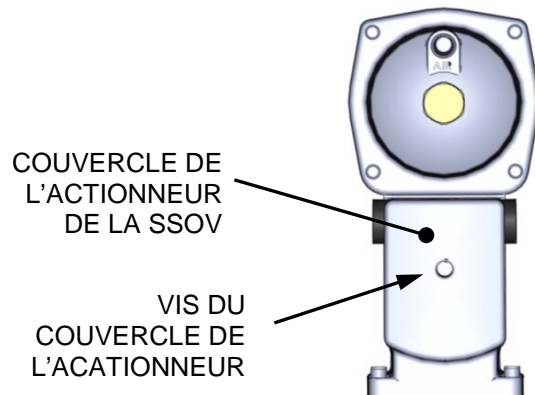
Emplacement du couvercle de l'actionneur de la SSOV
